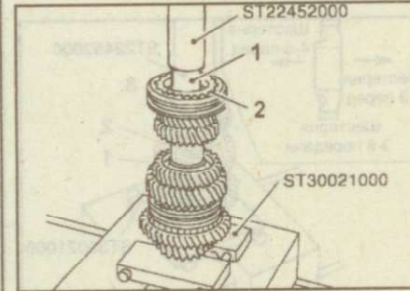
Установка втулки (1) шестерни передачи заднего хода и шестерни (2) передачи заднего хода
